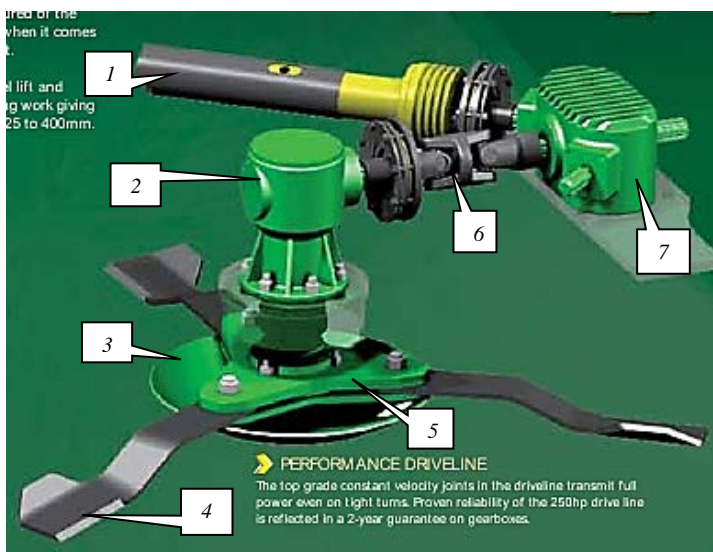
Ротор косилки Spearhead с приводом: 1 – вал; 2 – конический редуктор привода ротора; 3 – диск Anti-skalp; 4 – нож; 5 – несущая часть; 6 – вал привода центрального ротора; 7 – распределительный редуктор
